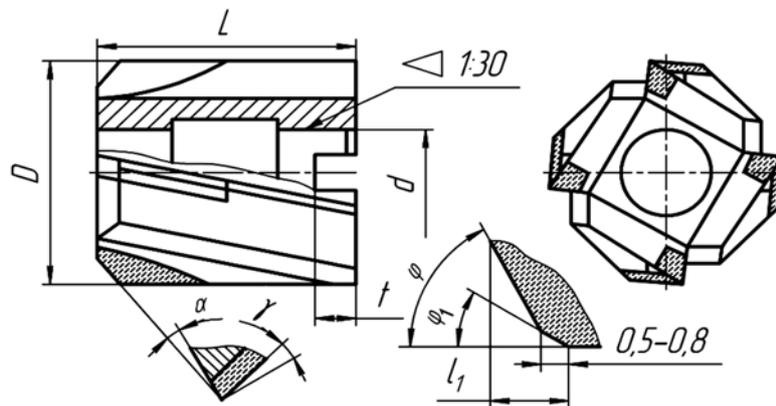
Насадной зенкер с напайными пластинками твердого сплава
